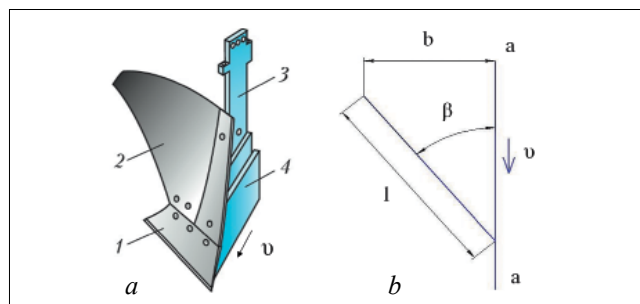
Корпус плуга (а) и схема его установки относительно стенки борозды (б): 1 – лемех, 2 – отвал, 3 – стойка, 4 – полевая доска, а-а – линия расположения стенки борозды; б – ширина захвата плужного корпуса; l – длина рабочего органа, подрезающего пласт; β – угол установки корпуса плуга относительно стенки борозды
